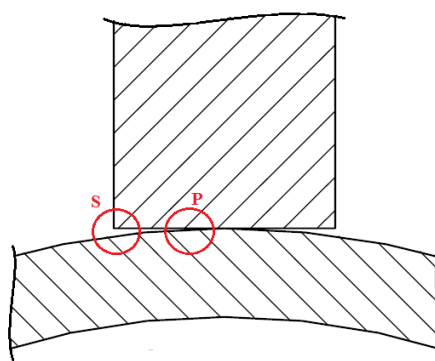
Representação esquemática dos componentes soldados assim como a região da ligação designada “à superfície”, S, e “em profundidade”, P.
